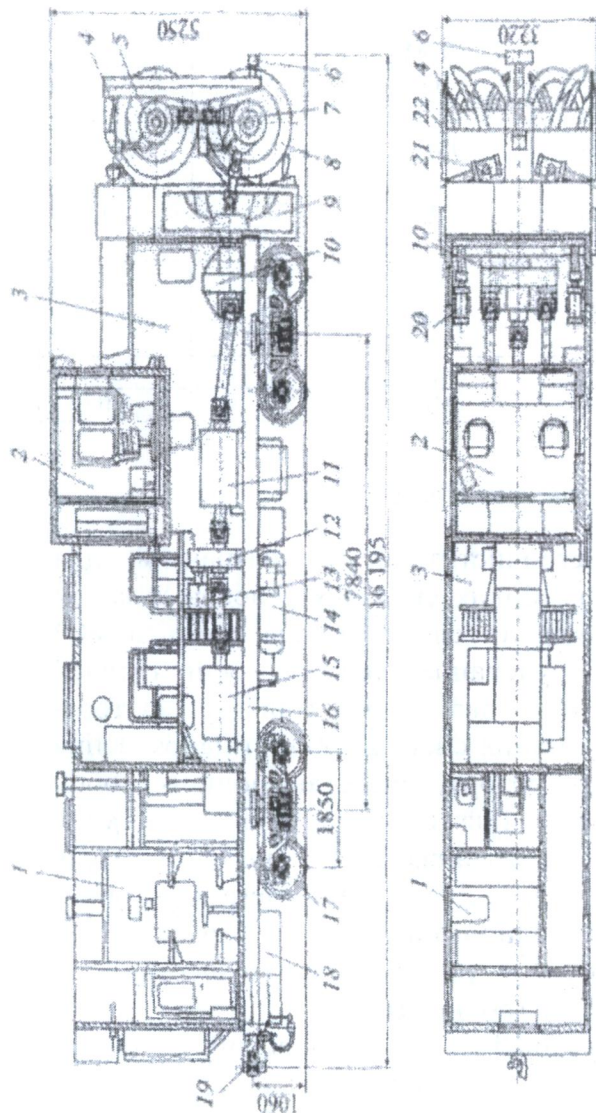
Фрезерно-роторный электрический снегоочиститель ФРС-2: 1 и 3 – бытовой и машинный отсеки; 2 – кабина управления; 4 и 8 – верхняя и нижняя фрезы; 5 и 7 – конические редукторы; 6 – фланец для установки жесткой автосцепки; 9 – выбросной ротор-метатель; 10 и 12 – цилиндрические редукторы; 11 и 15 – электродвигатели привода выбросного ротора и фрез; 13 – генератор; 14 – тормозная система; 16 – рама; 17 – ходовые тележки; 18 – противовес; 19 – автосцепка; 20 – привод подрезного ножа; 21 – пневматический цилиндр поворота боковых крыльев; 22 – боковое крыло
